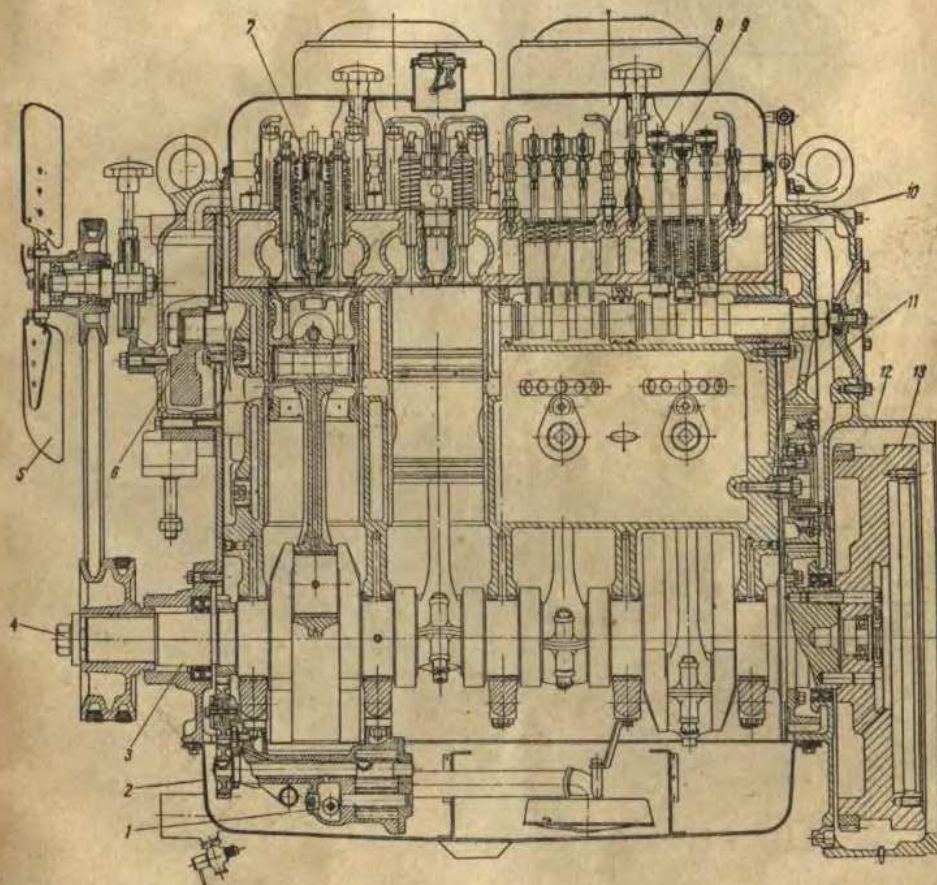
Продольный разрез двигателя ЯАЗ-М204А:
